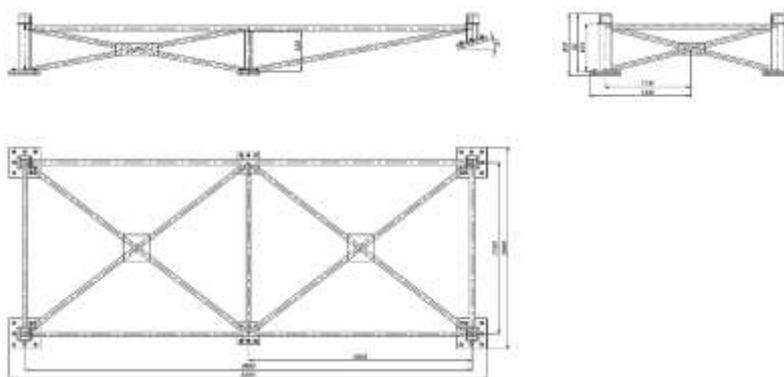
Чертеж рамы под рефрижераторный контейнер
